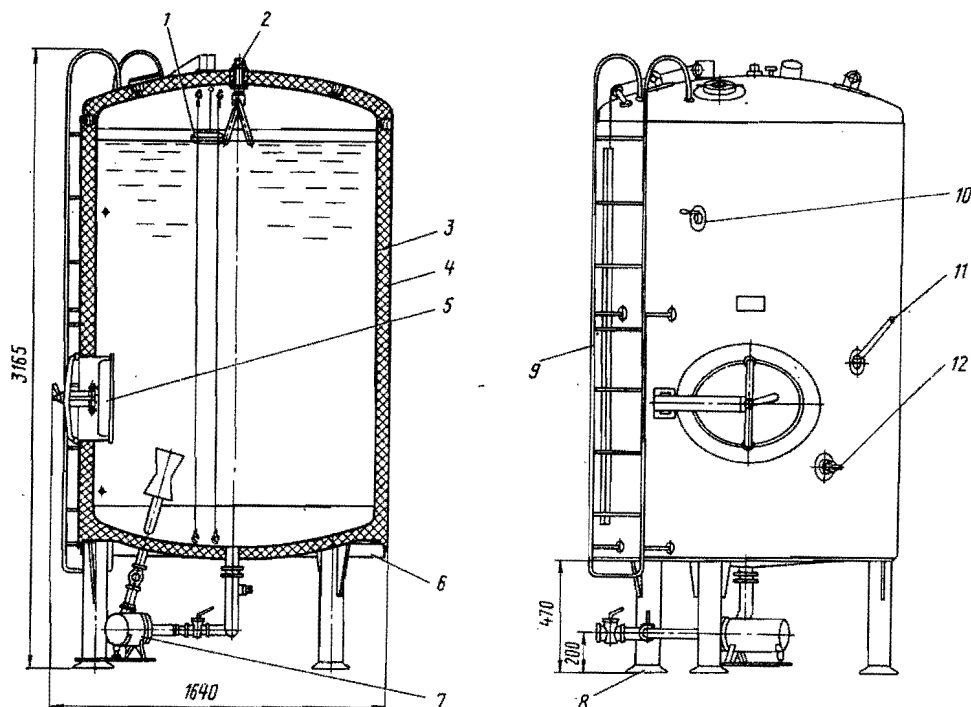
Общий вид резервуара марки В2-ОМВ-2,5:
